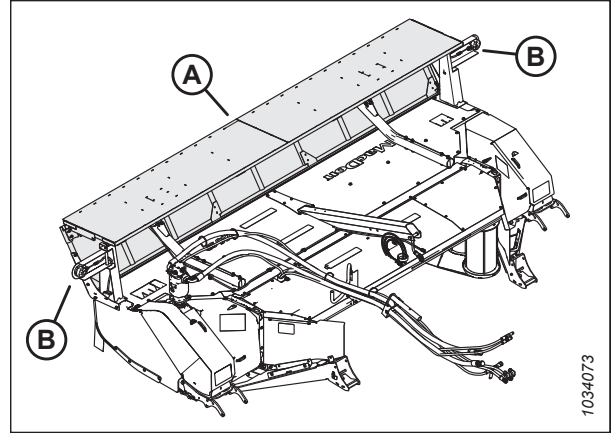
Противоосыпательный щиток и фонари — транспортировочное положение
